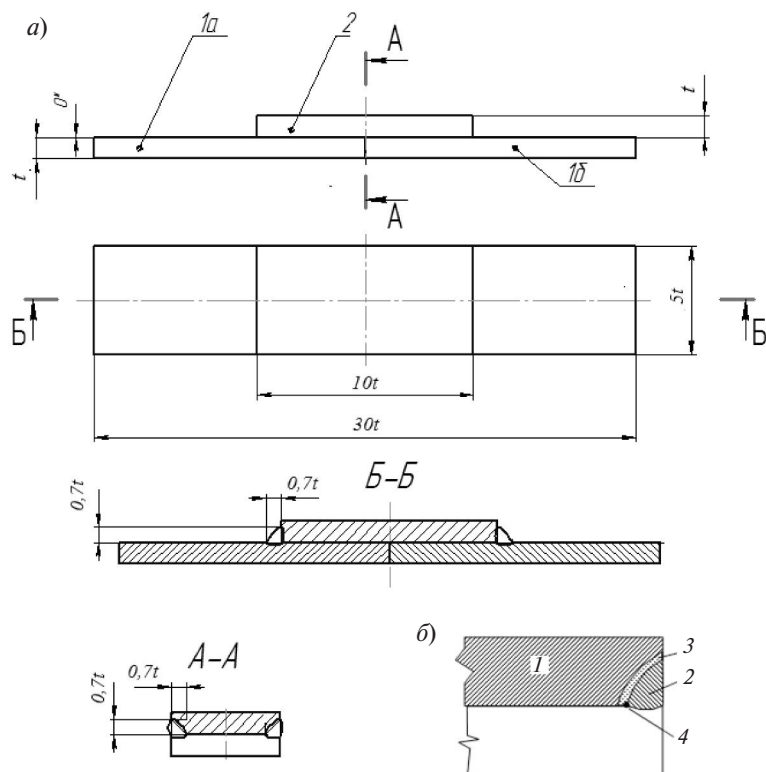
Образец для испытаний: *a* — чертеж образца; *б* — схема распределения зон в образце: 1 — основной металл пластин; 2 — наплавленный металл; 3 — зона термического влияния; 4 — точка максимальной концентрации напряжений
